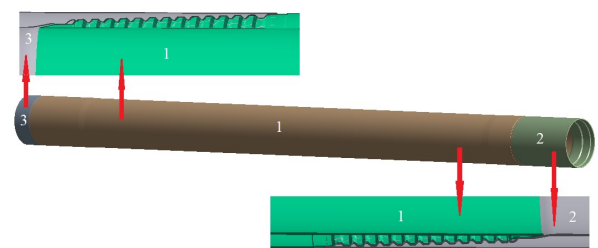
Ескіз збірної циліндричної конструкції з різьбовими з'єднаннями по краях:
